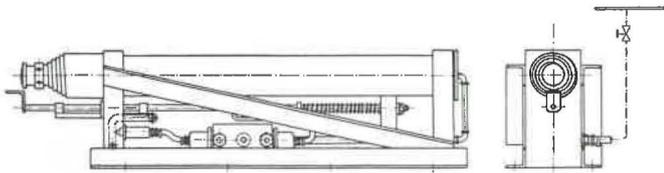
Appareil de rebroussement à piston pneumatique Strunk.
